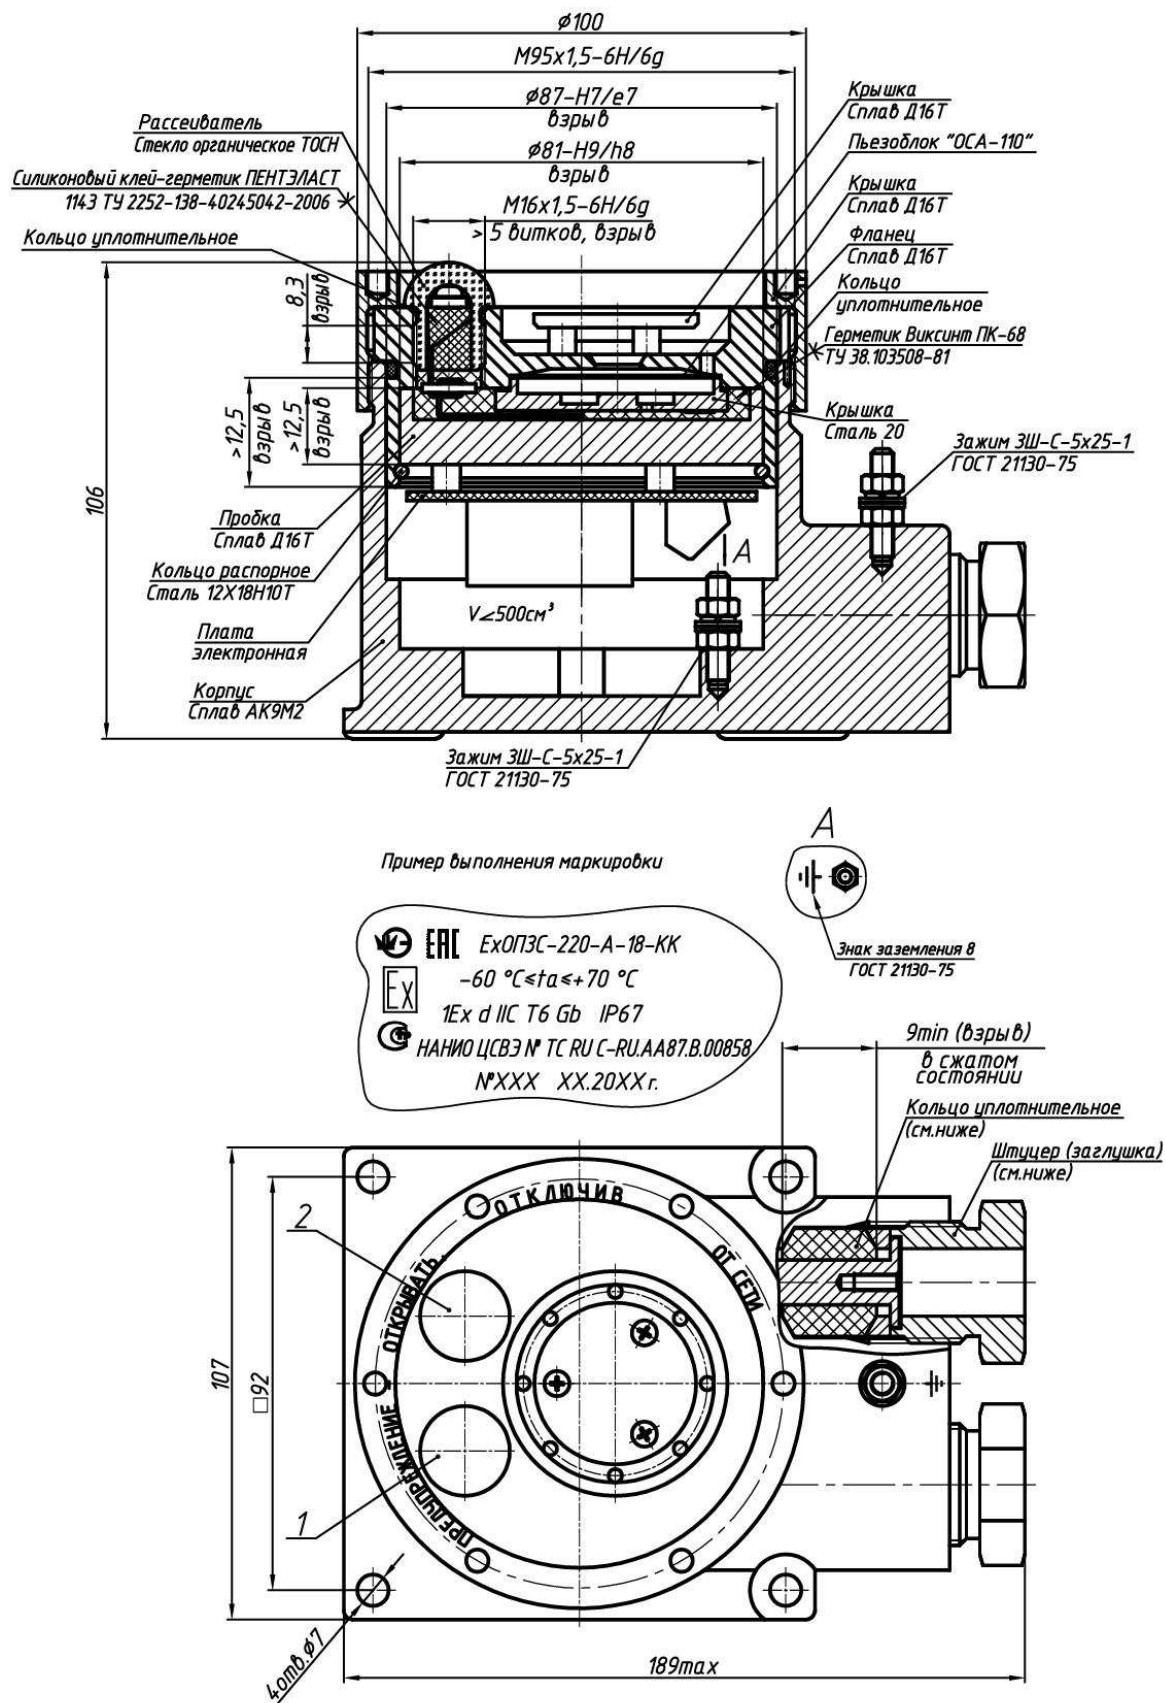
Габаритный чертёж Оповещателей моделей ExOPЗС-A в корпусе из алюминиевого сплава, совмещённый с чертежом взрывозащиты
